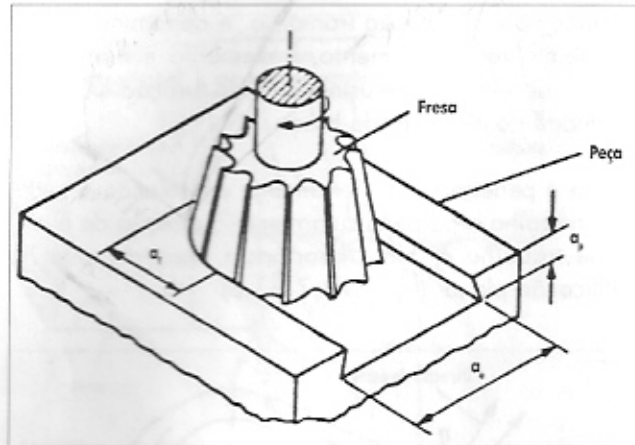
Profundidade de usinagem a_p , penetração de trabalho a_e e penetração de avanço a_v no fresamento frontal
